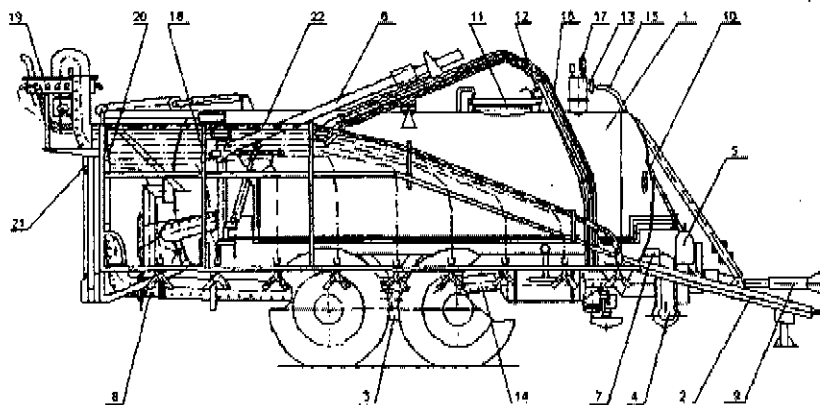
Схема штанговой машины для внесения жидких органических удобрений МЖТ-6Ш: 1 – цистерна; 2 – дышло; 3 – подвеска балансира; 4 – центробежный насос; 5 – вакуумный насос; 6 – штанга заправочная; 7 – устройство переключающее; 8 – коммуникация; 9 – карданная передача; 10 – указатель уровня удобрений в цистерне; 11 – люк; 12 – клапан вакуумный; 13 – клапан жидкостный; 14 – трубопровод; 15 – трубопровод вакуумный; 16 – рукав заправочный; 17 – вакуумметр; 18 – штанга распределительная; 19 – делительная головка; 20 – каретка; 21 – растяжка; 22 – шланг-понижитель
